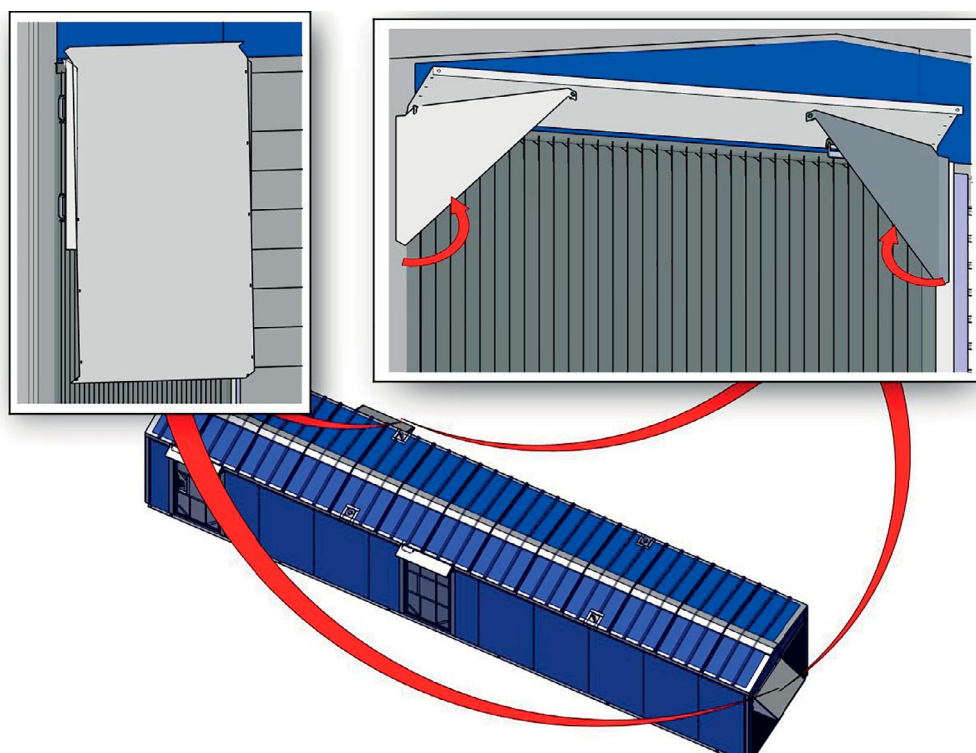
Общий вид преобразователя частоты со схемой сборки козырьков над жалюзи забора воздуха
